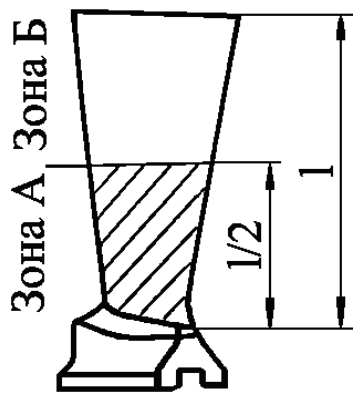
Рабочая лопатка компрессора низкого давления (КНД) двигателя Д36 с разбивкой на зоны, где повреждения допускаются и не допускаются: зона А – повреждения не допускаются; зона Б – повреждения допускаются определенного размера.
